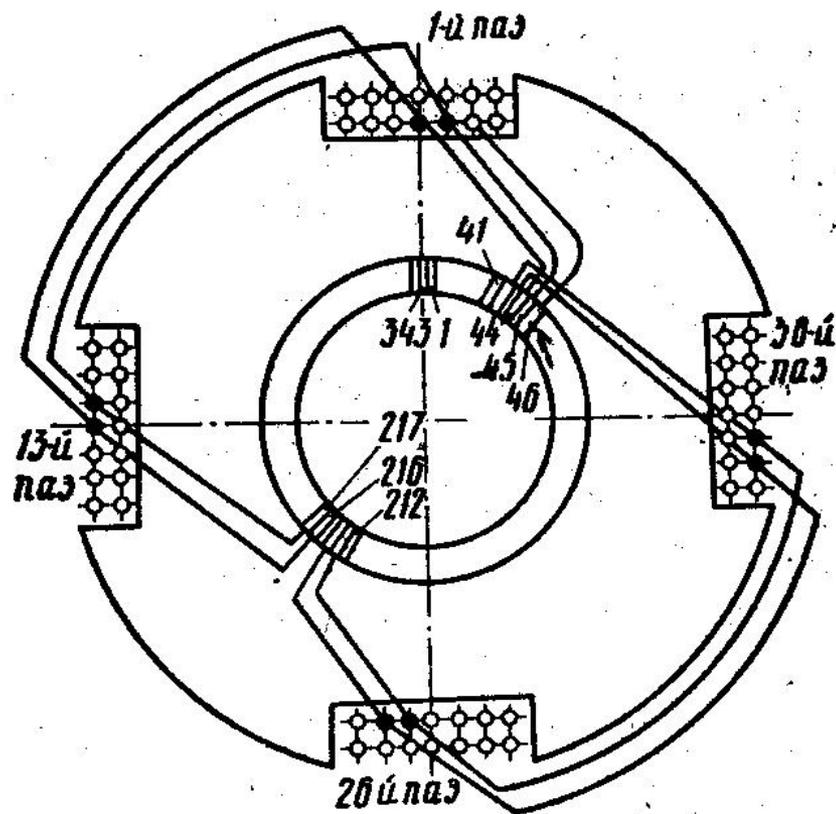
Схема соединения обмотки якоря двигателя преобразователя НБ-436В
